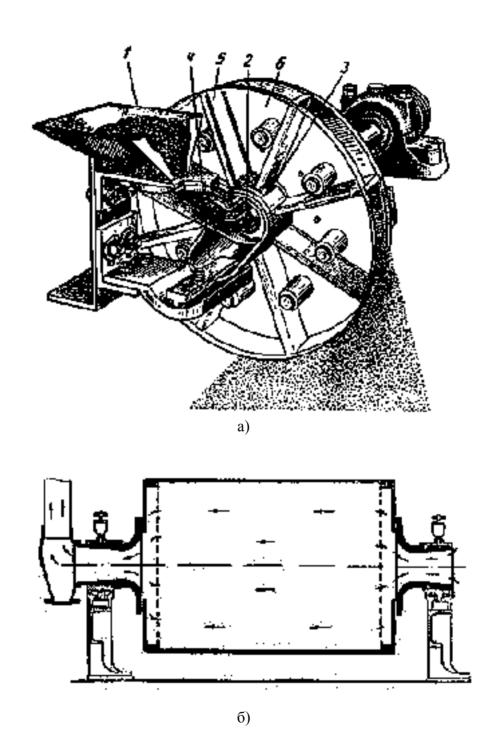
Оборудование для очистки отливок: а) дробеметное лопаточное колесо дробеметной камеры (1 — воронка с дробью, 2 — распределительные лопатки, 3 — отверстие в коробке для выбрасывания дроби, 4 — неподвижная коробка (труба), 5 — рабочие лопатки, 6 — диски колеса) б) галтовочный барабан.
